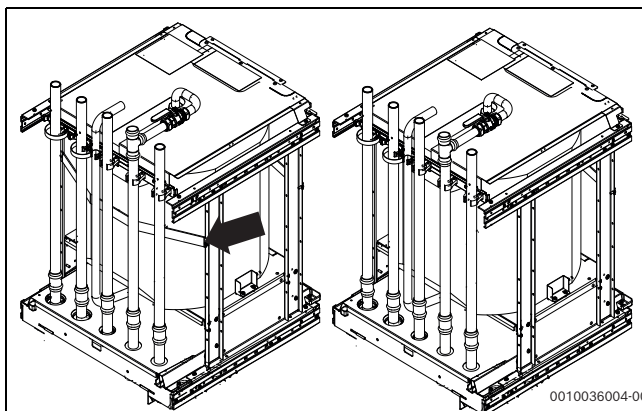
Smontaggio della staffa di fissaggio posteriore
